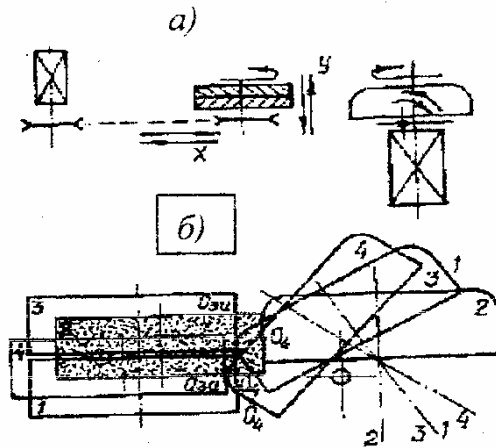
Схема движения инструмента и детали при обработке наружной поверхности (а) и положение инструмента и детали в процессе обработки (один цикл) (б). Процесс обработки деталей обеспечивается многосвязным рычажным механизмом (рис.3).
